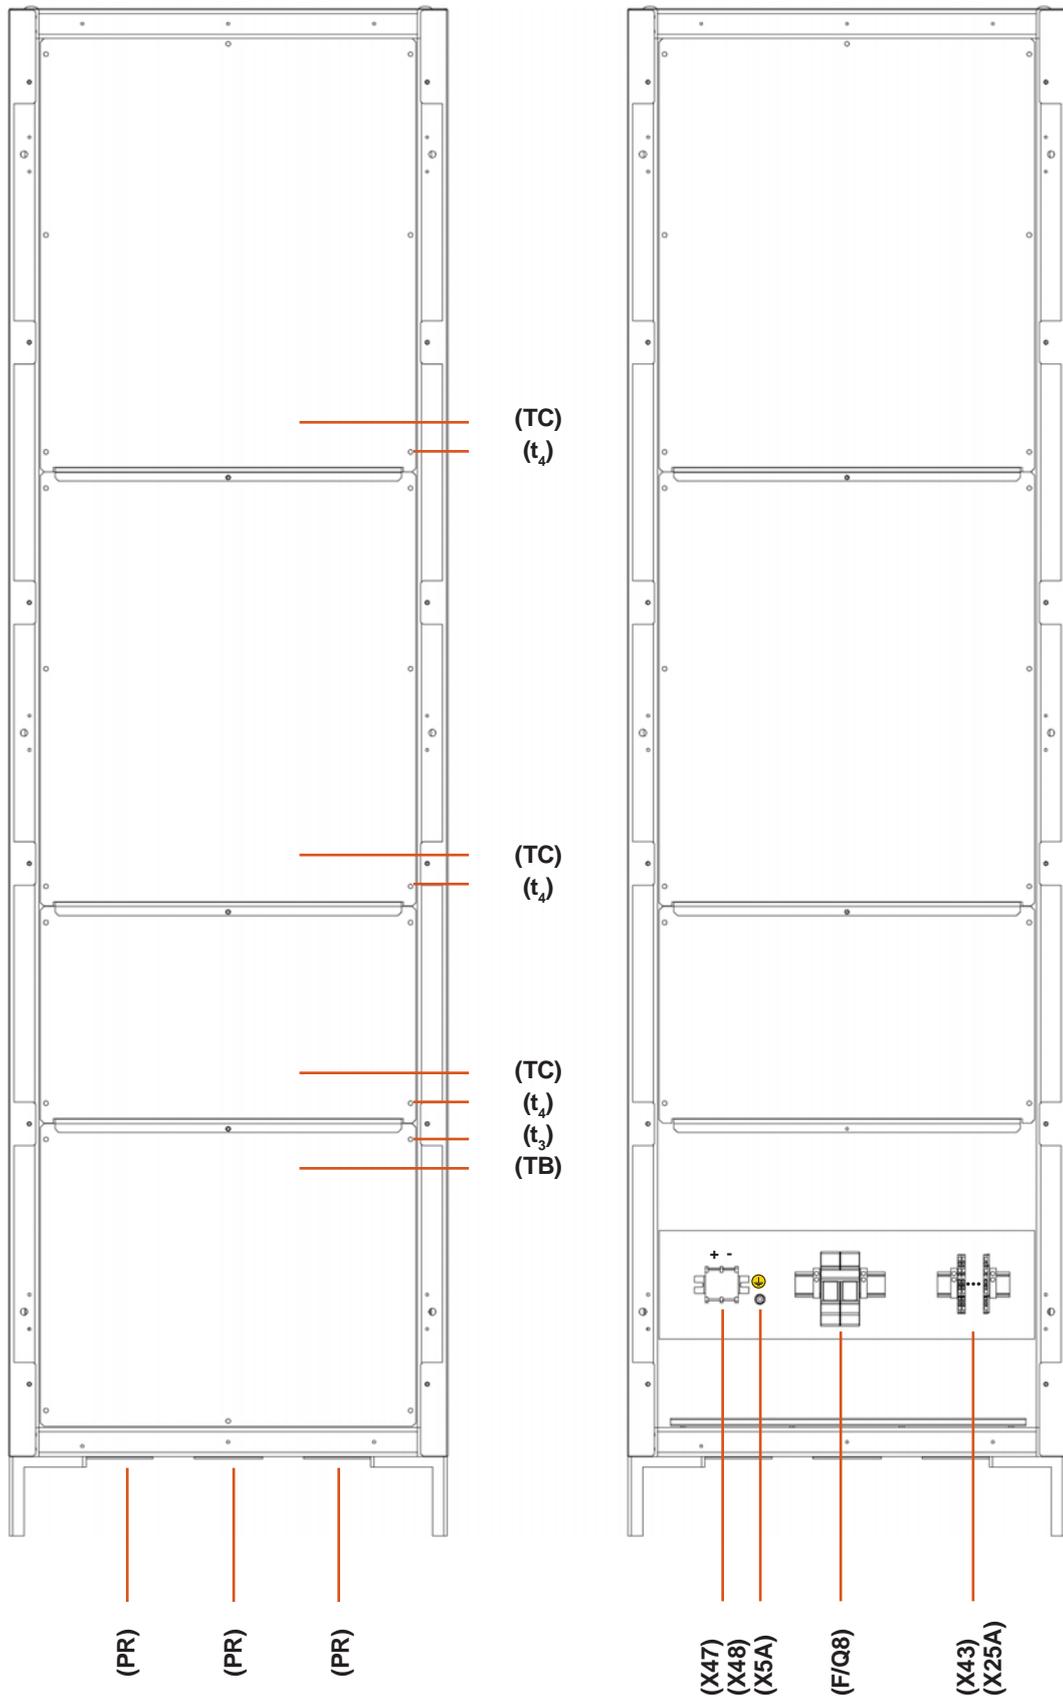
Vue frontale armoire de batteries de 605x605x2115 mm.
